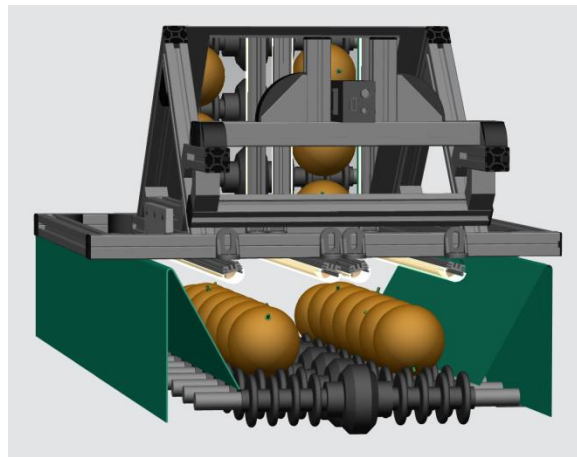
Diseño del sistema de visión sobre una línea de rodillos
